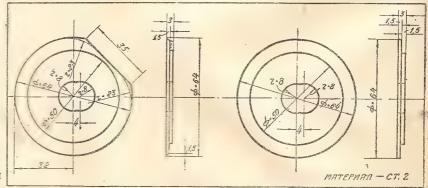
Шайбы головон: поворачивающейся (слева) и неподвижной (справа) стоек механизма автомата для смены пластинок.
